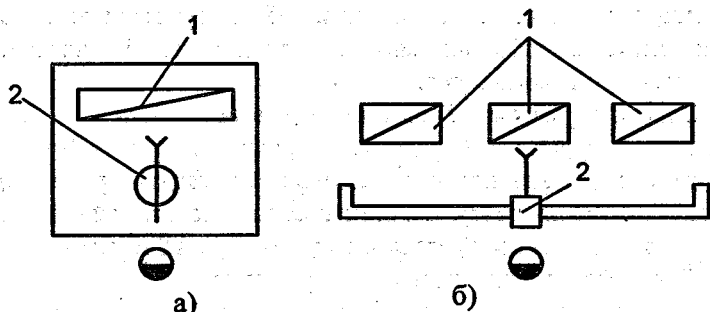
Схема расположения оператора и оборудования РТК: а) с разделением зон; б) с совмещением зон; 1 – станок; 2 – ПР.
